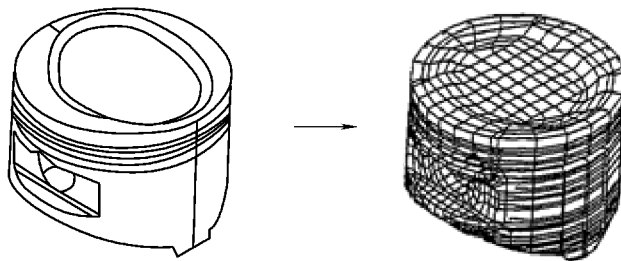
活塞的几何 CAD 模型和 CAE 模型
